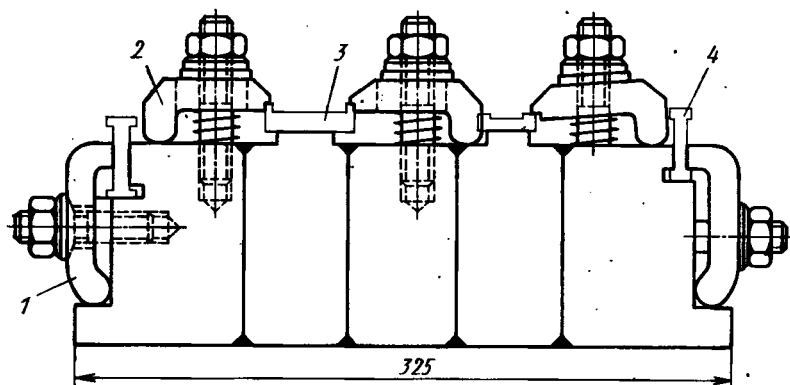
Схема приспособления для строгания заготовок зигзагообразных пружин
